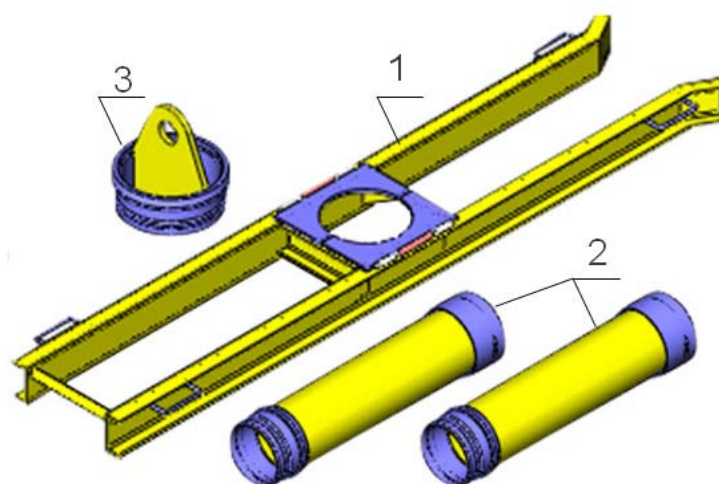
Комплект оборудования, применяемого при бетонировании траншеи методом «стена в грунте»: 1 — балка опорная, служит для опирания бетонолитных труб в процессе монтажа и демонтажа; 2 — секции бетонолитных труб; 3 — звено подъемное, применяется для монтажа бетонолитных труб в процессе бетонирования
